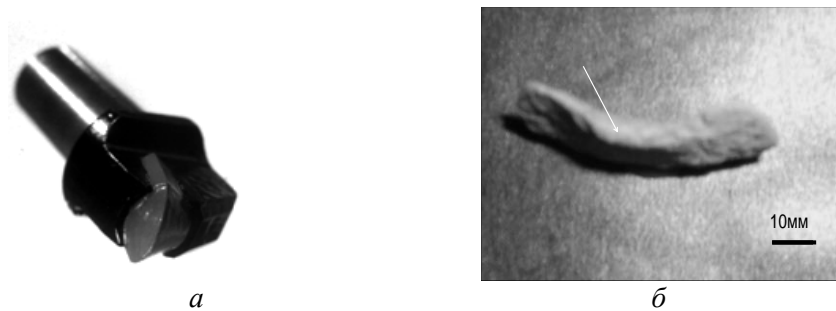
Загальний вид: твердосплавного різця РП-221 – а; фрагмент продуктів руйнування пісковіку Теревовлянського родовища твердосплавним різцем РП-221, (вид спереду) – б
